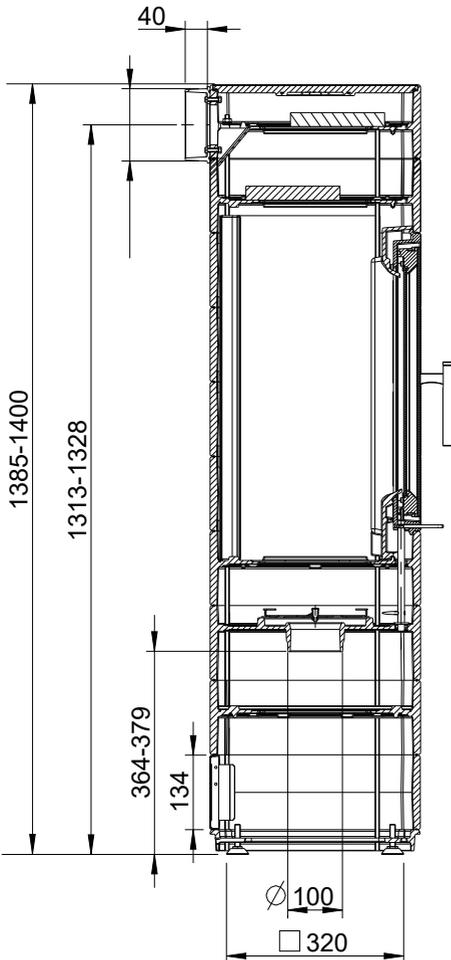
Sortie des fumées, dimensions pour une buse raccordée vers l'arrière- CORNA hoch, CORNA hoch tec ou CORNA hoch ES
